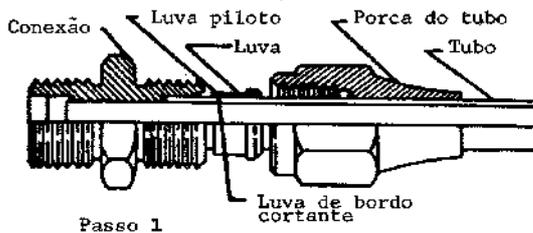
Pré-montagem de um conjunto de tubo sem flange.
